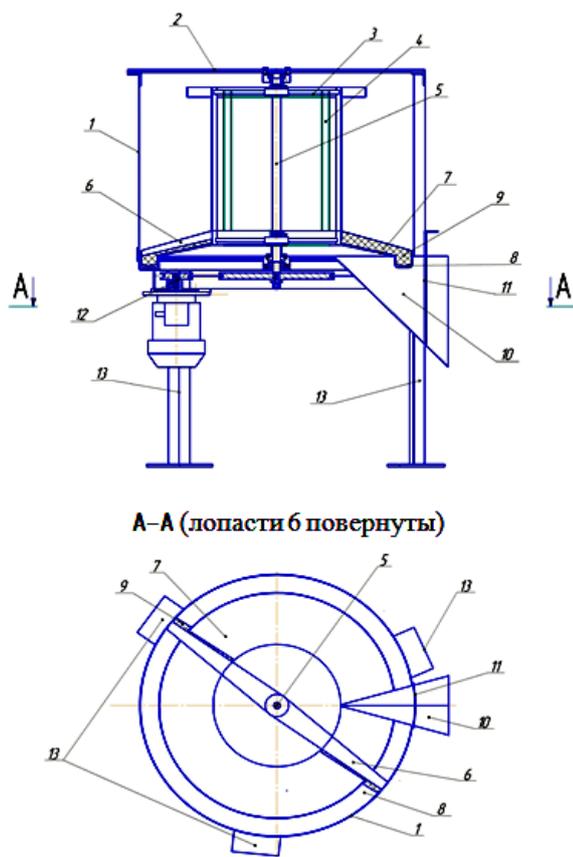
Конструктивно-технологическая схема комбинированного агрегата: 1 – цилиндрическая емкость; 2 – крышка; 3 – ротор; 4 – кассета; 5 – вал; 6 – лопасть; 7 – дно; 8 – канавка; 9 – эластичный элемент; 10 – V-образный лоток; 11 – заслонка; 12 – привод; 13 – опора
